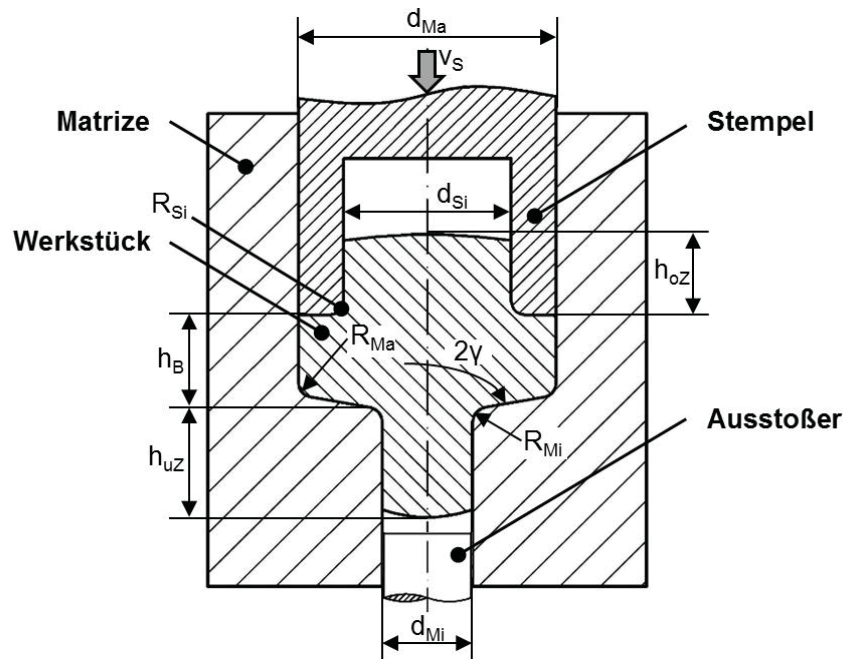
Prinzipskizze des VV-VR-FP mit einem bewegten Werkzeugelement (Stempel)
